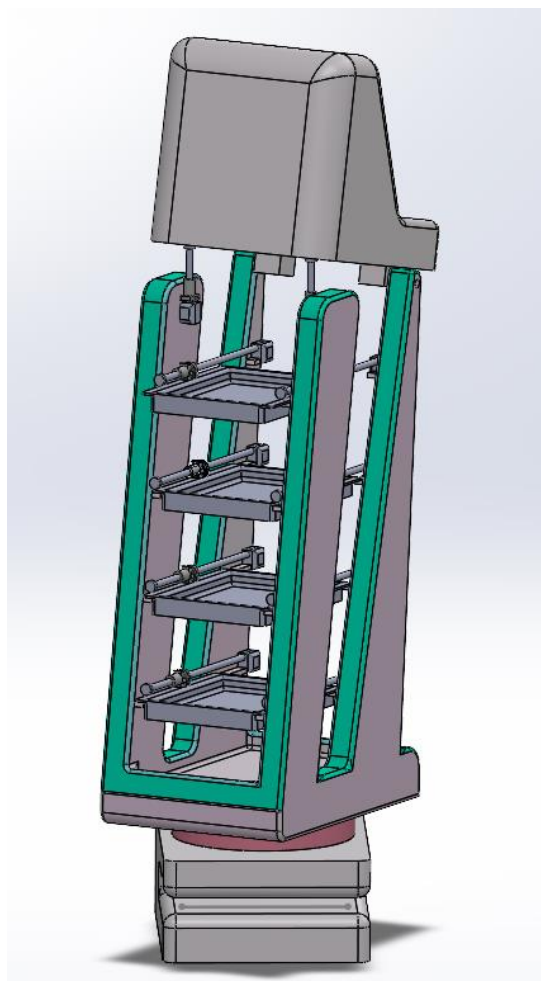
Widok po skosie obrazujący mechanizm śrubowo-toczny na złożeniu w położeniu krańcowym.
